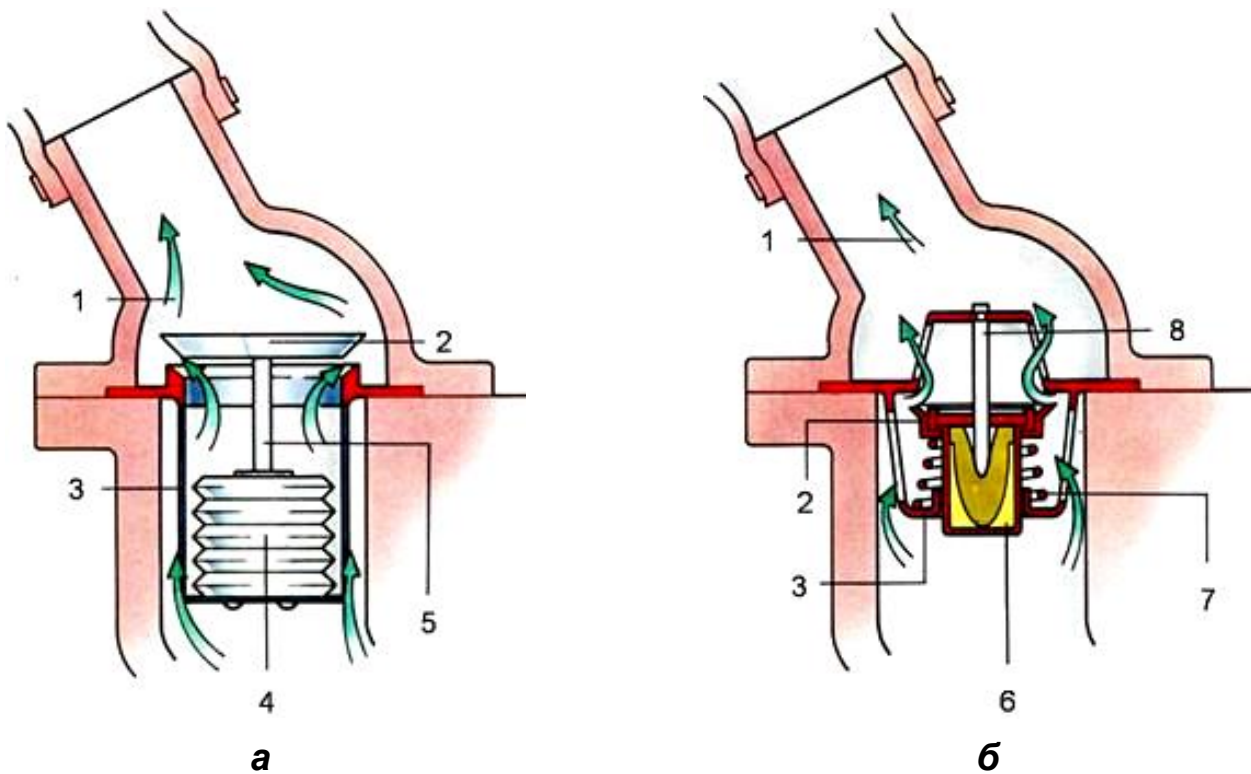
Термостат: а – рідинний; б – з твердим наповнювачем; 1 – патрубок до радіатора; 2 – клапан; 3 – мідний або латунний балон; 4 – гофрований циліндр (сильфон); 5 – шток; 6 – термочутлива речовина; 7 – поршень
